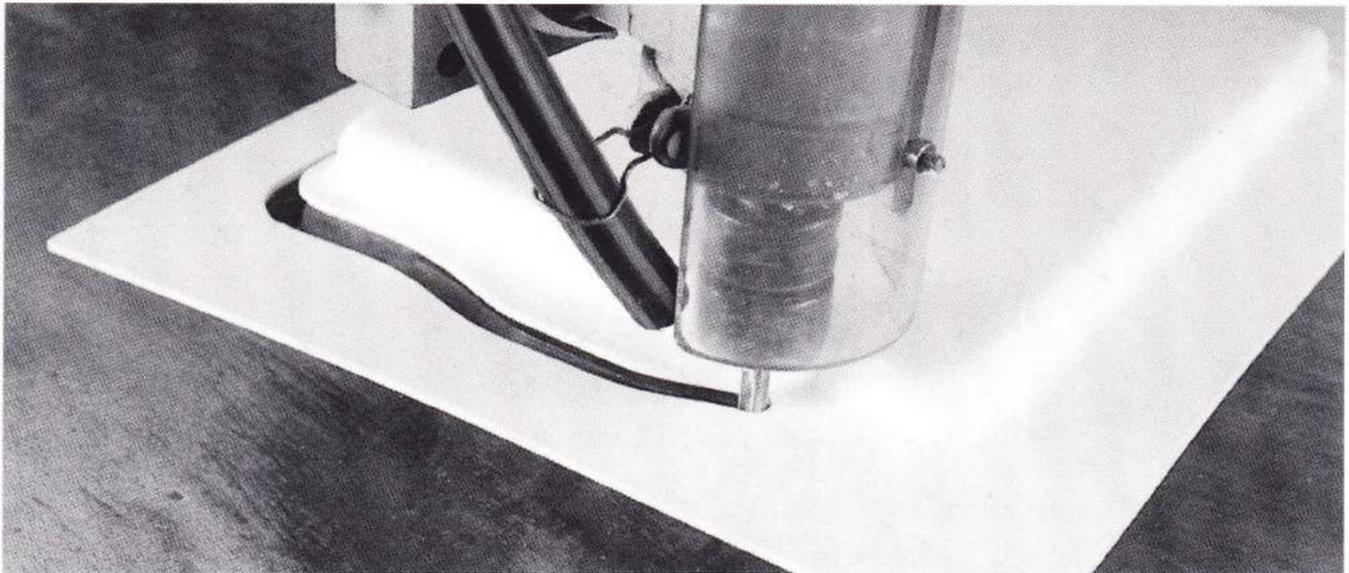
Обрезка отформованной детали методом фрезерования по шаблону
